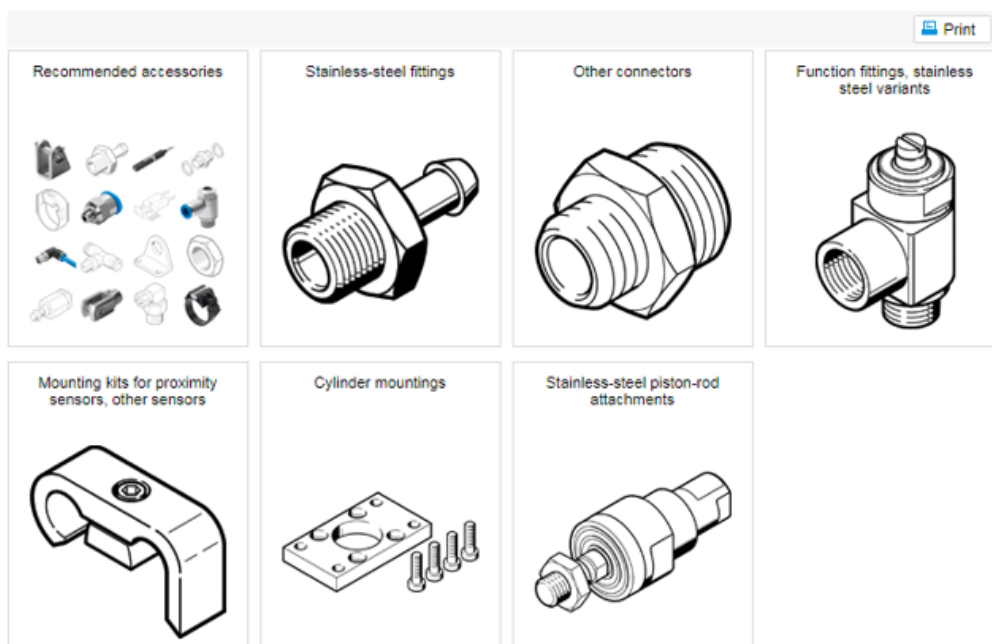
Os componentes e acessórios que fazem parte de cada braço pneumático. [31]
